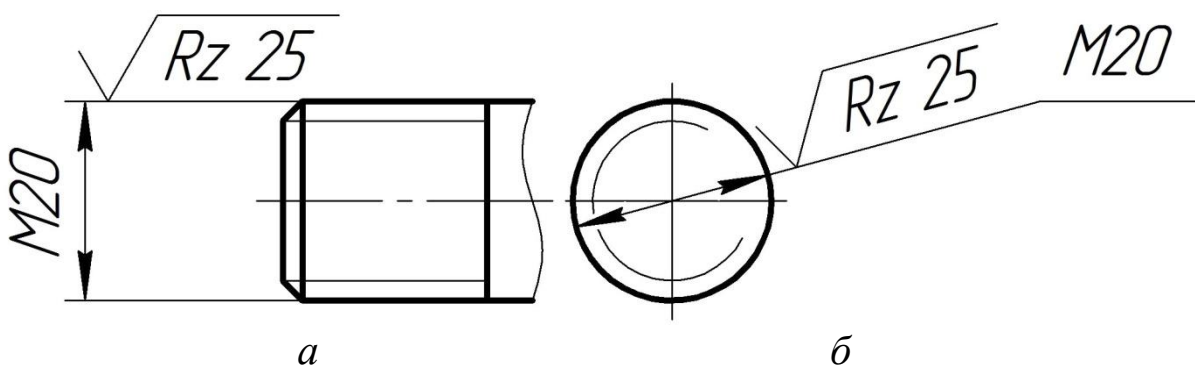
Обозначение шероховатости поверхности резьбы
